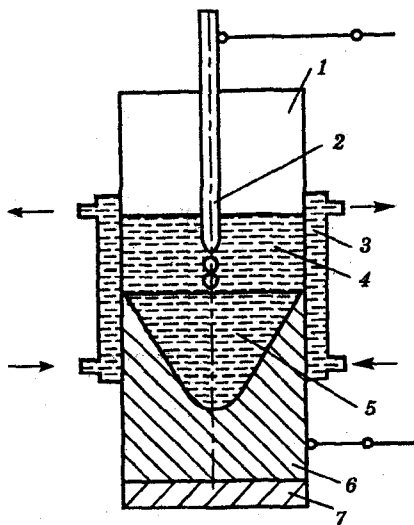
Схема процесса электрошлаковой сварки
